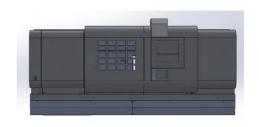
CKA6180 数控机床 Fig.2 CKA6180 CNC machine tool
